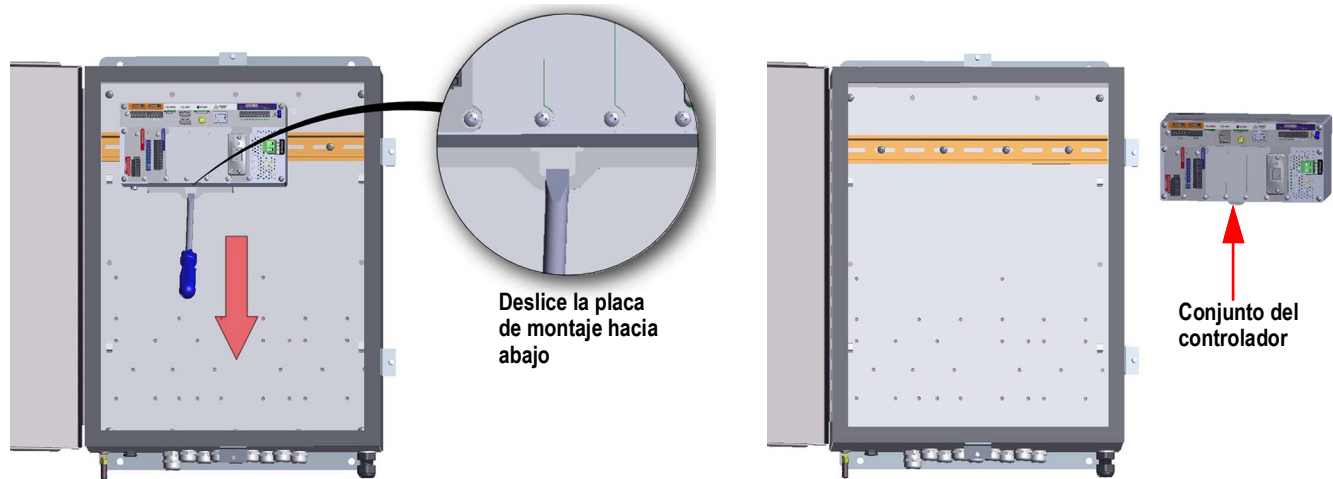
Desmontaje del conjunto del controlador - Alojamiento para pared
